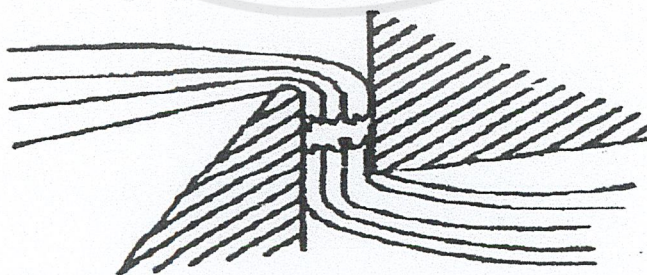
แสดงลักษณะการตัดแบบ Chip forming cut
